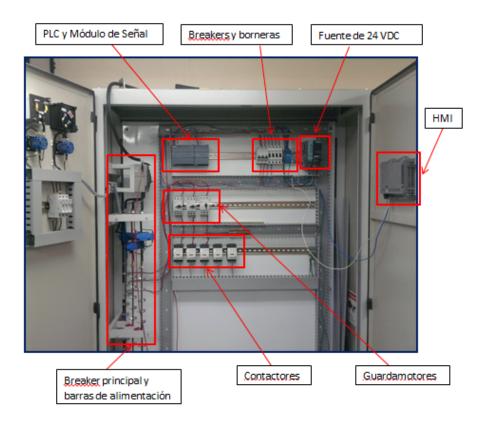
Instalación y cableado de los primeros elementos del tablero. Fuente: Autores
